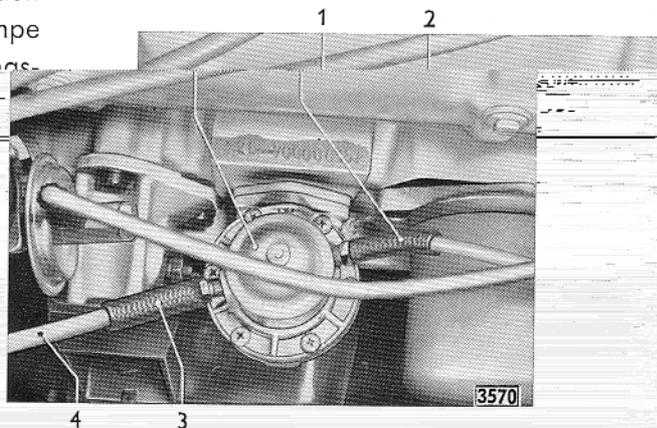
Kraftstoffpumpe eingebaut und Kraftstoffleitungen angeschlossen
